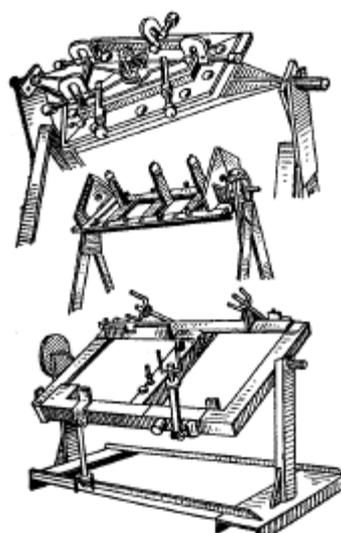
Приспособления, снабжённые постоянными упорами, гнёздами и крепёжными устройствами для фиксации правильного взаимного расположения
